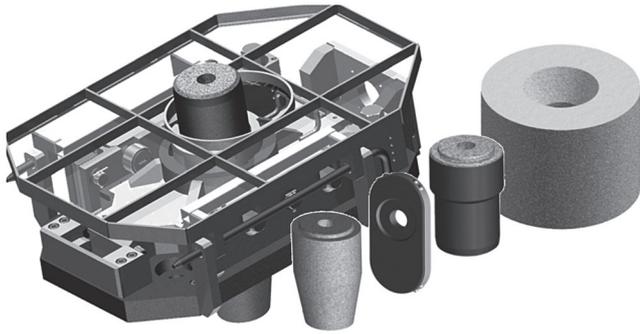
Шиберный затвор ВТ-30 с комплектом огнеупоров проволоку с различными наполнителями; трайб-аппарат малогабаритный одно-, двух-, трех- и четырехручьевого для подачи порошковой проволоки в ковш [3].
